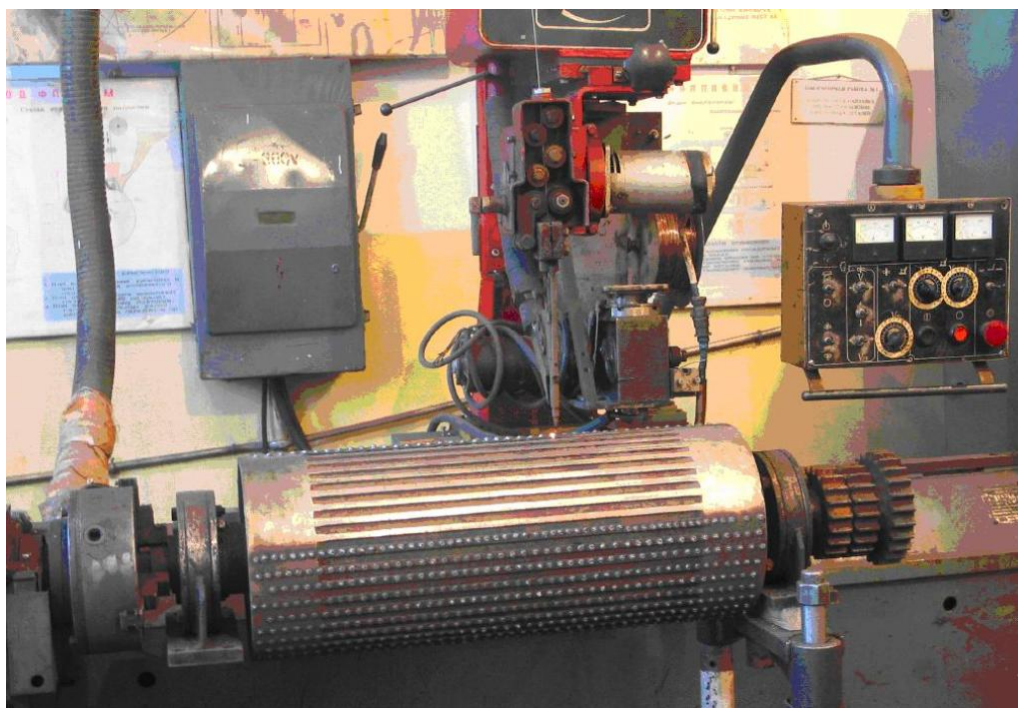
Установка для наплавки шипов с роликом, наплавляемым вдоль цилиндрической поверхности
